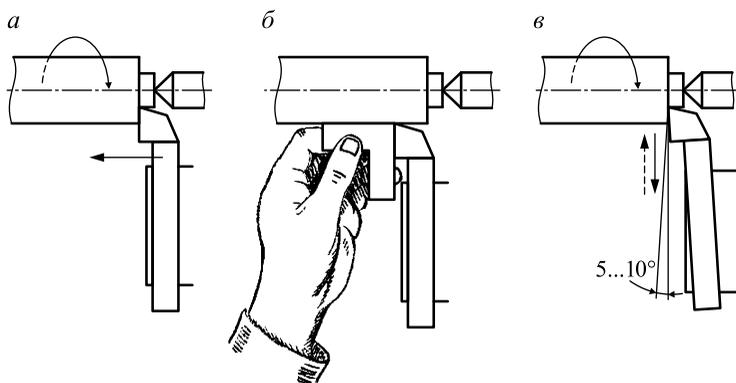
Положение резцов при обработке ступенчатых поверхностей
